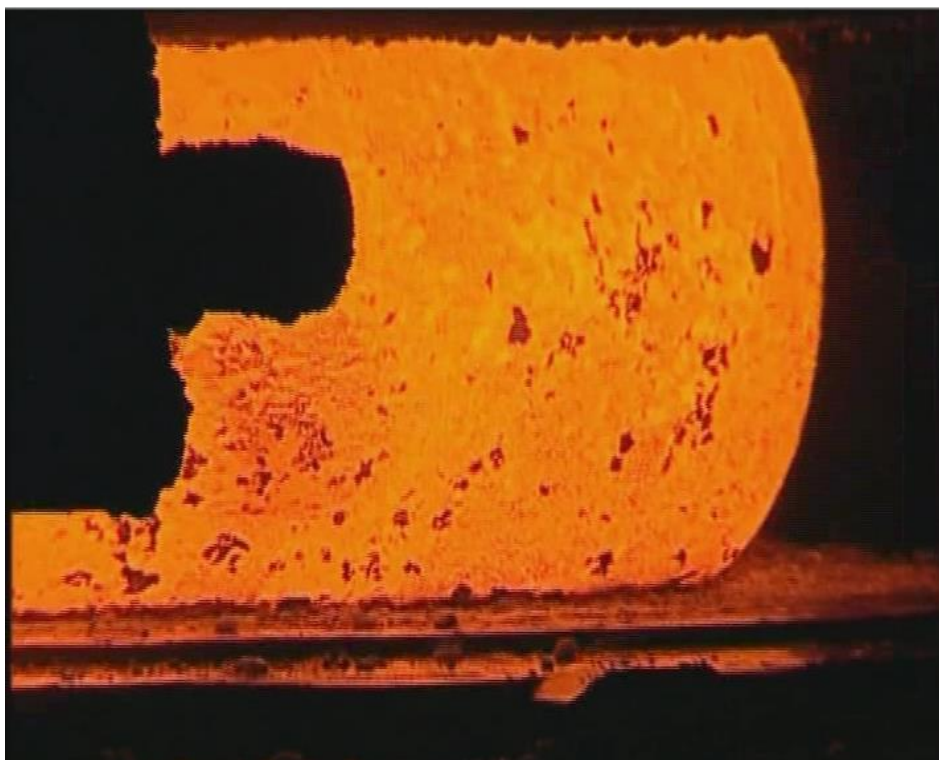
Предварительная осадка заготовки на прессе силой 20 МН
